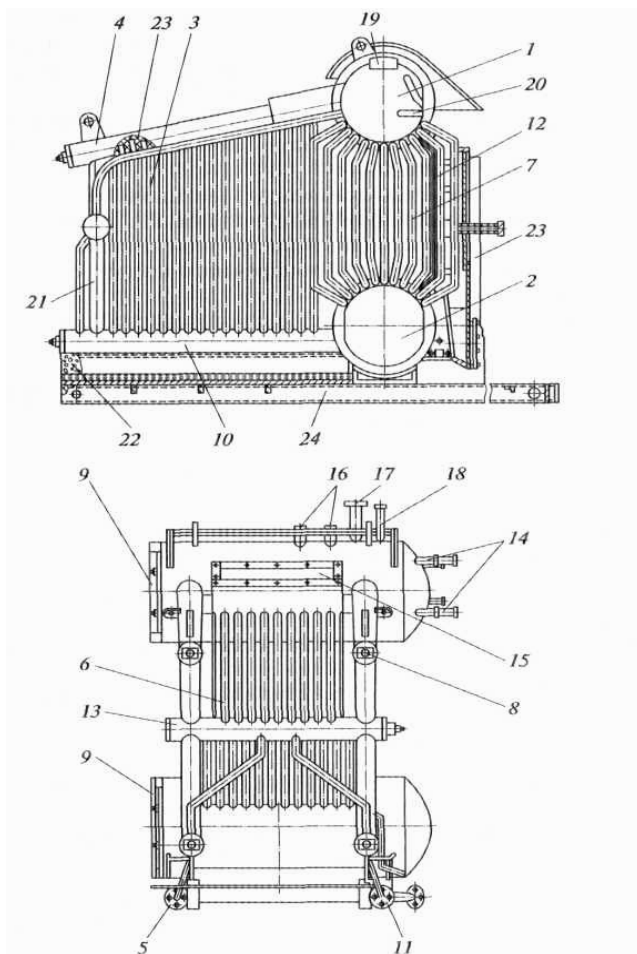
Устройство парового водотрубного котла низкого давления с естественной циркуляцией Е-1/9Г: 1 – верхний барабан; 2 – нижний барабан; 3 – боковые топочные экраны; 4, 10 – коллектор; 5, 11 – продувочный штуцер; 6 – потолочный экран; 7 – кипяtilьные трубы; 8 – лючек для осмотра коллекторов; 9 – люки для осмотра барабанов; 12 – перегородки в конвективном пучке; 13 – фронтальной коллектор; 14 – патрубок водоуказательной арматуры; 15 – газоотводящий патрубок котла; 16 – предохранительный клапан; 17 – главный паротводящий штуцер; 18 – трубка крепления манометра; 19 – сепарационное устройство; 20 – труба подвода питательной воды; 21 – переходник горелочного устройства; 22 – заливка огнеупорным бетоном; 23 – теплоизоляция; 24 – несущая рама
